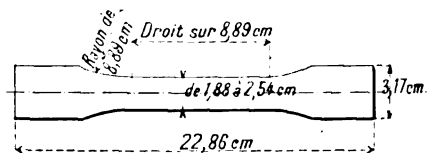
Eprouvette pour les essais de résistance à la traction et d'allongement sur les planches.
